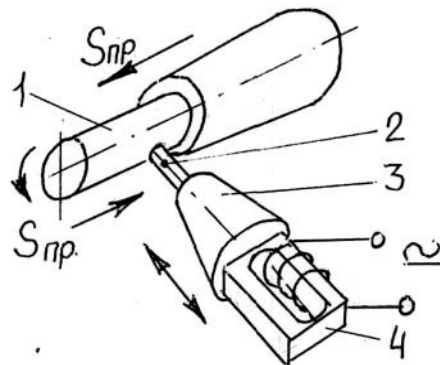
Схема різання: 1 – заготовка; 2 – інструмент; 3 – концентратор; 4 – УЗ перетворювач
